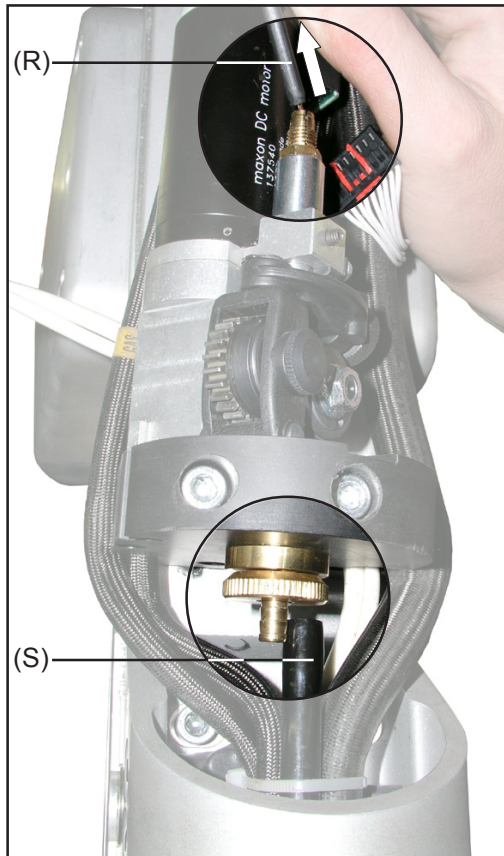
Drahtführungsseele und Schutzschlauch befestigen
